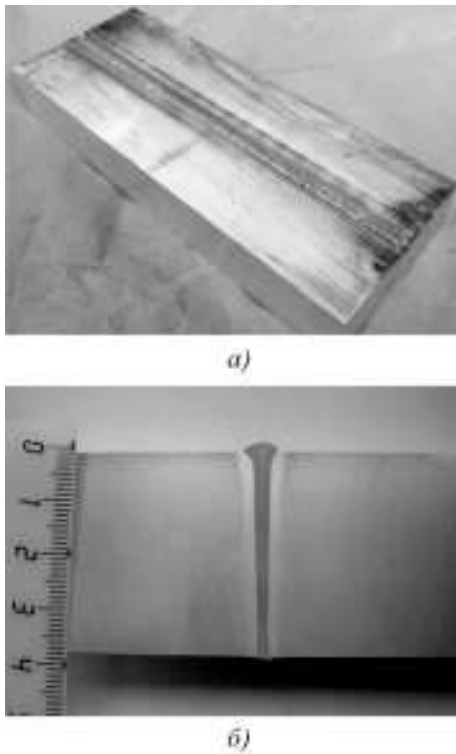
Сварной образец (а) и макроструктура сварных соединений, выполненных электронно-лучевой сваркой (б)
